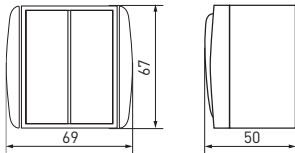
Габаритные размеры 2-клавишного выключателя
